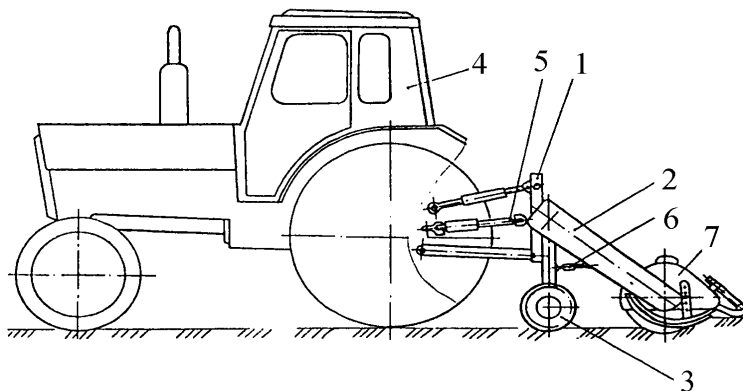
Фреза почвенная ФП-1,3: 1 – рама; 2 – поводок; 3 – опорное колесо; 4 – трактор; 5 – карданная передача; 6 – стяжка; 7 – фрезерный барабан
